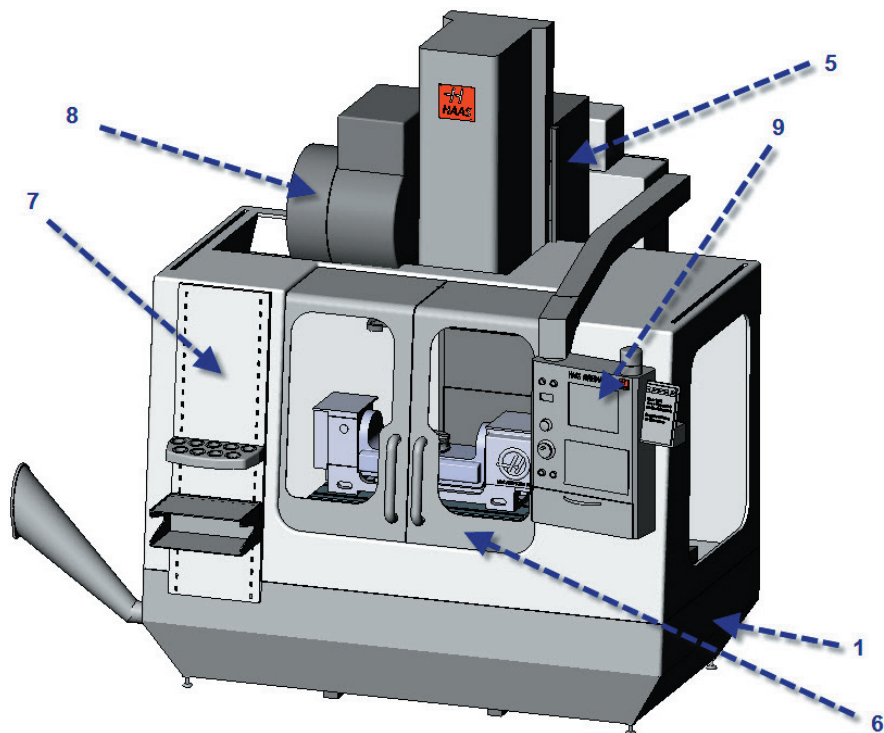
Корпус вертикально-фрезерного станка с ЧПУ
